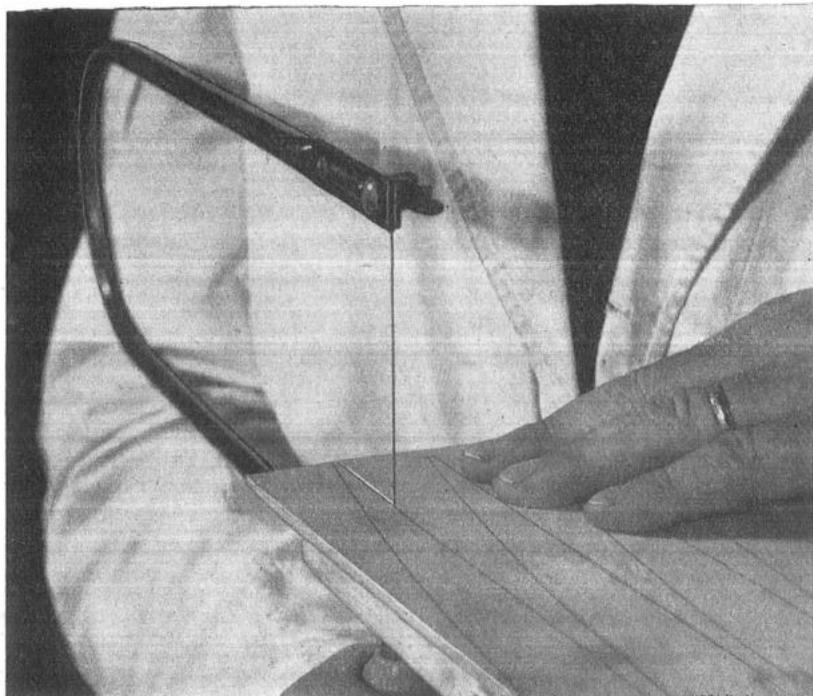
Per un taglio perfetto appoggiare l'archetto della sega sul braccio.
